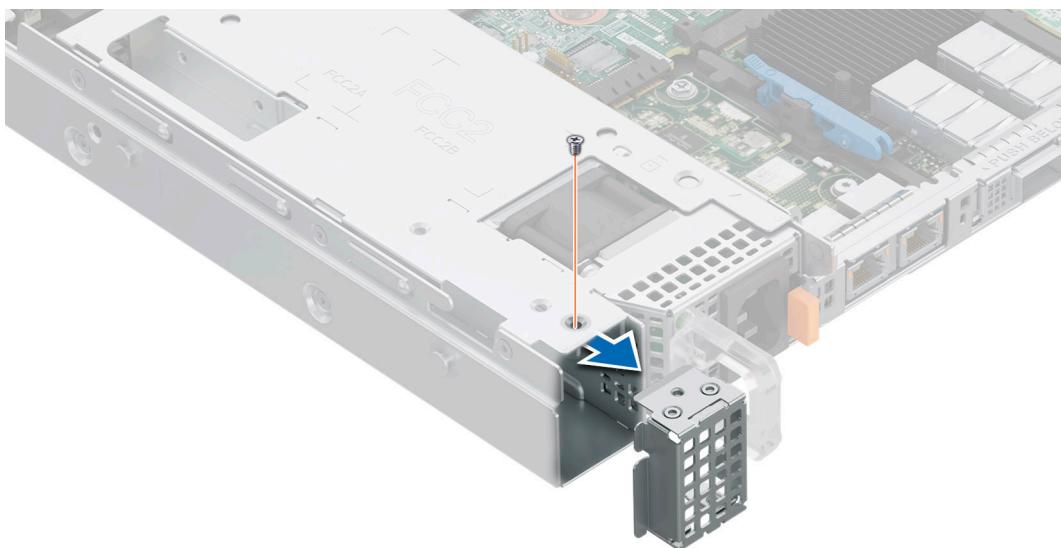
Entfernen des BOSS-N1-Modulplatzhalters
